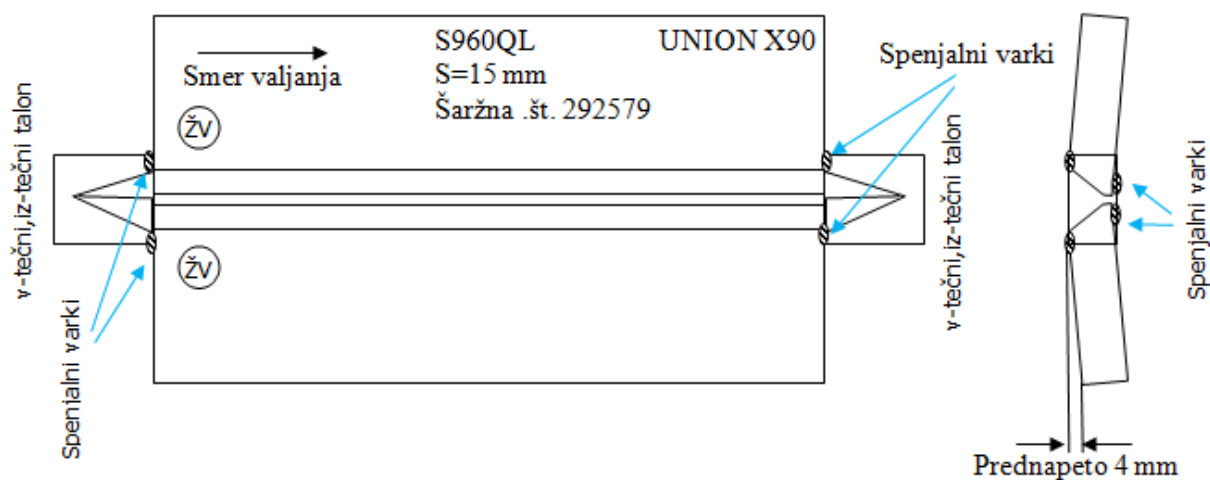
Skica priprave sestavnih elementov vzorca VP 0118 P/BK
